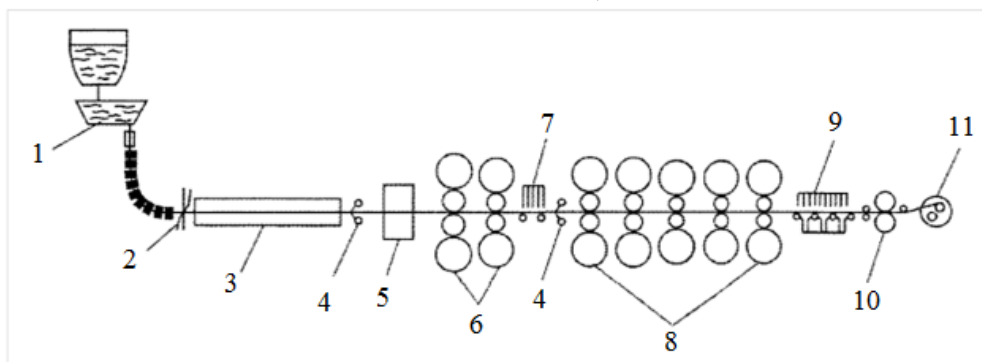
Схема агрегата DSP [2]: 1 – машина для лиття тонких слябів; 2 – маятникові ножиці; 3 – нагрівальна тунельна піч; 4 – установка для видалення окалини; 5 – кліть з вертикальними валками; 6 – чернові кліти; 7 – установка для переміжного охолодження; 8 – безперервна чистова група клітей; 9 – холодильник; 10 – летучі ножиці; 11 – моталка
